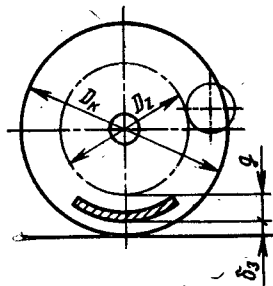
Схема зубчатой передачи тягового электродвигателя
